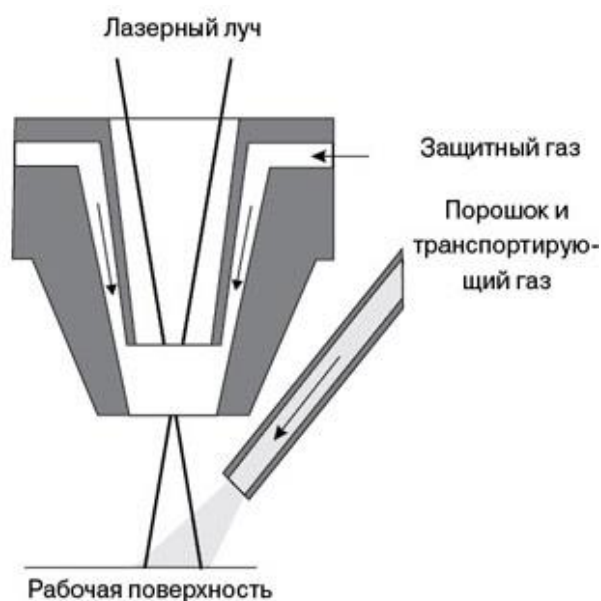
Схема лазерной наплавки с боковой подачей порошка
